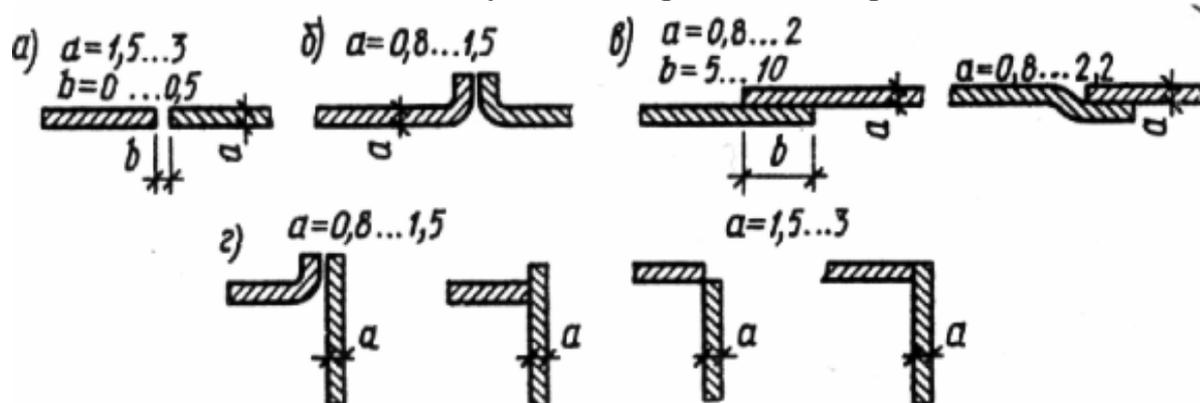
Виды сварных соединений металлических воздуховодов:
